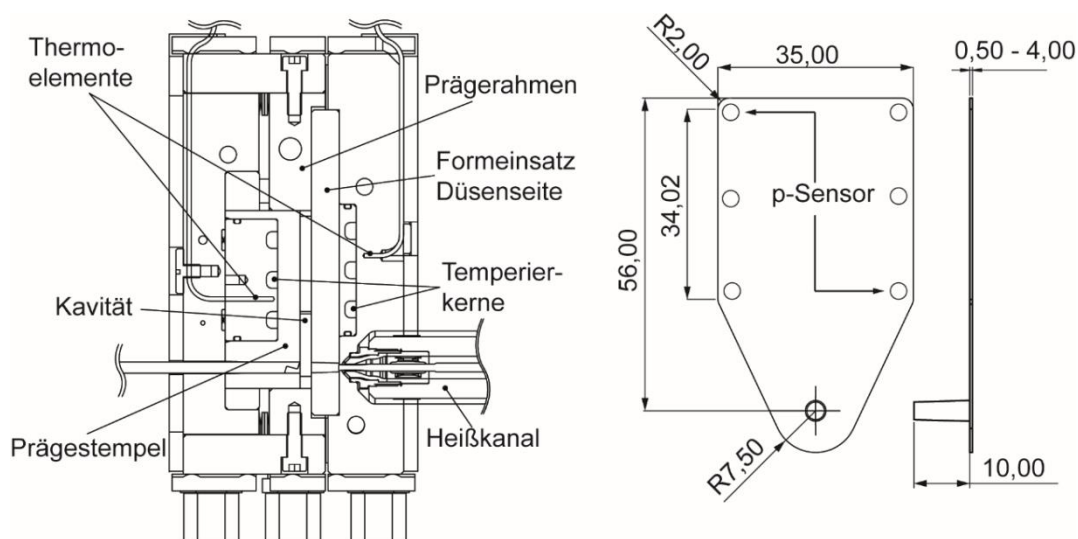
links: Schematischer Aufbau des Versuchswerkzeuges
